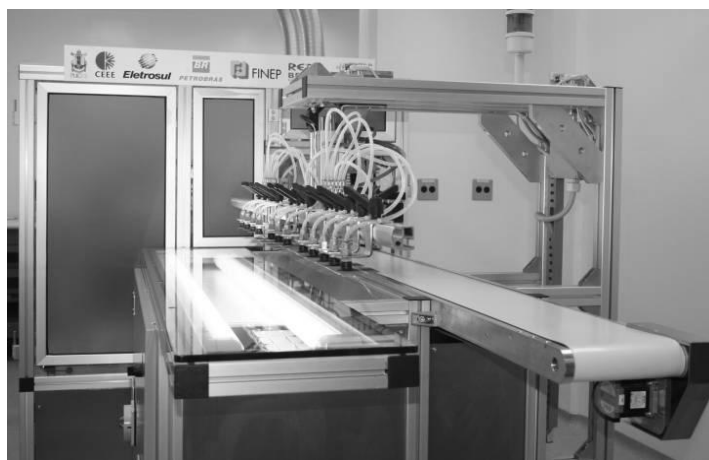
Equipamento usado para a soldagem das tiras de células solares.
